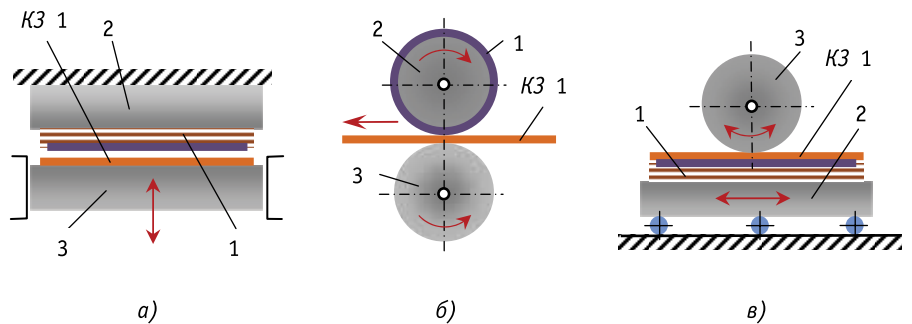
Різновиди штанцювальних пресів: тигельний (а); ротатійний (б); плоскоциліндровий (в)
